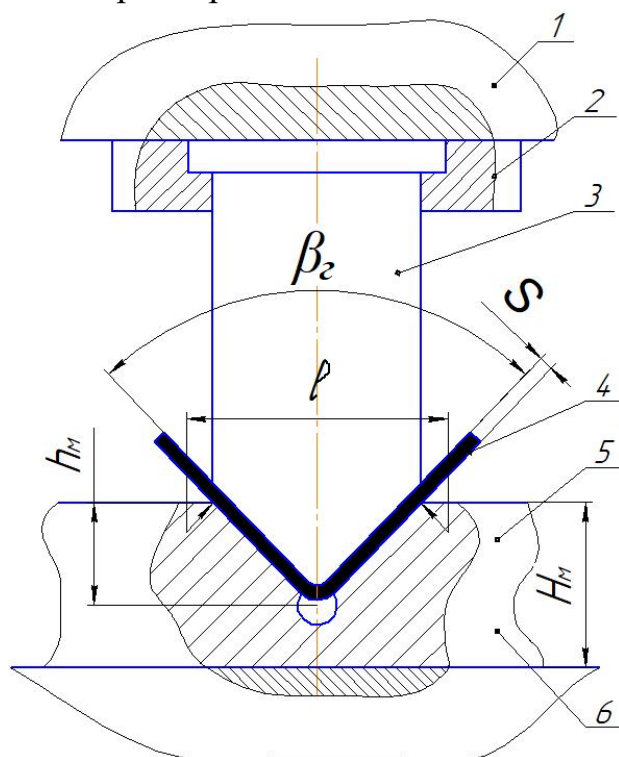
Схема открытого штампа для одноугловой V-образной гибки: 1- ползун; 2-пуансонодержатель; 3-пуансон; 4- образец; 5-матрица; 6-стол прессы.
